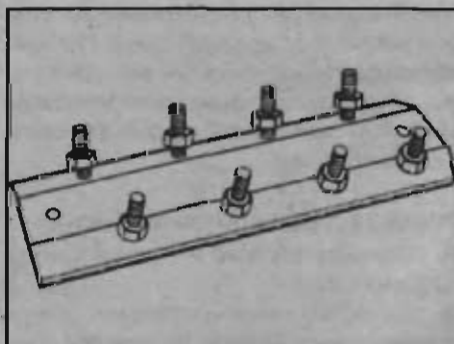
Специальный инструмент, используемый для отвода коромысел от кулачков распределительного вала
